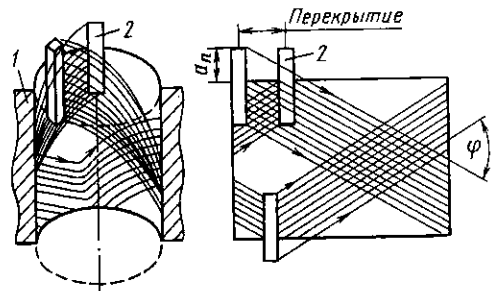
Схема формообразования цилиндрической поверхности 1 при хонинговании абразивными брусками 2:  $\varphi$  — угол скрещивания,  $\alpha_n$  — перебор
